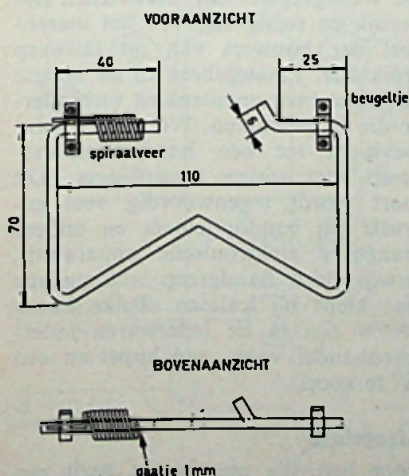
Kaststeun; 3 à 4 mm ϕ , gegalvaniseerd ijzerdraad.
